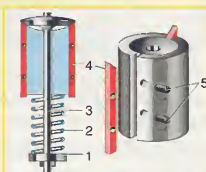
Приспособление для обработки клапанов: 1 — шайба; 2 — пружина; 3 — клапан; 4 — резец; 5 — винт.
